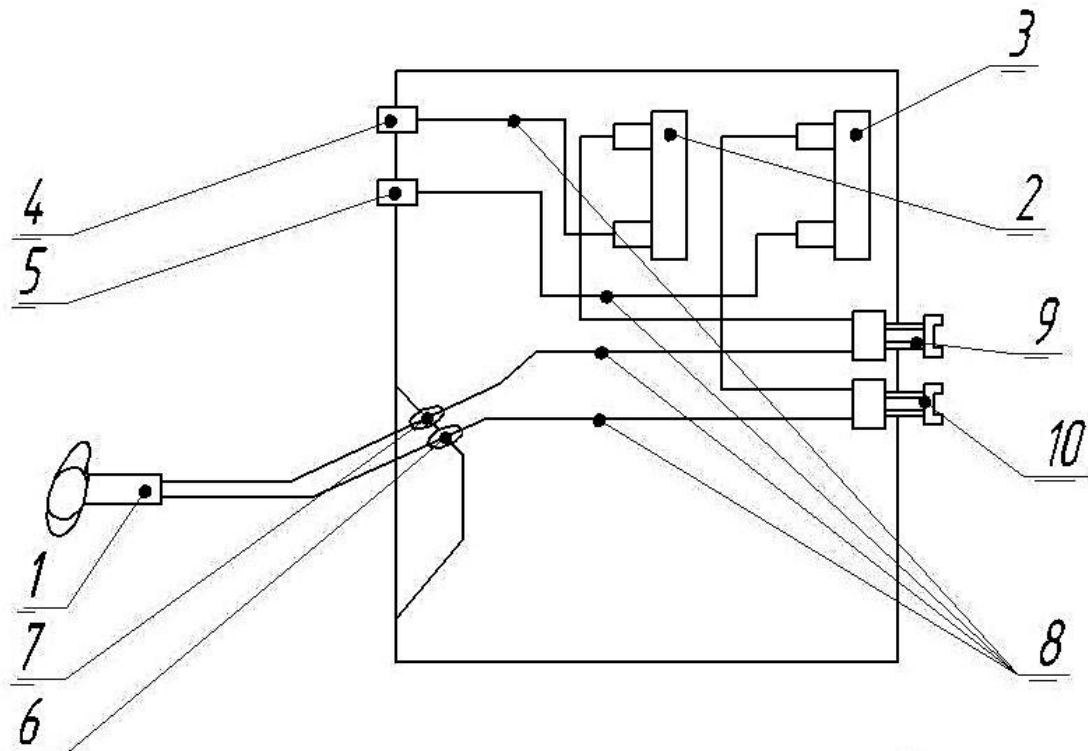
Електрична принципова схема установки для плазмового зварювання типу МПУ - 4
